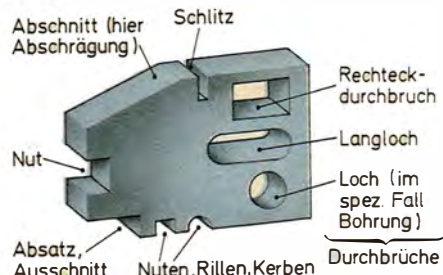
Begriffe für Teilformen (Einarbeitungen)
